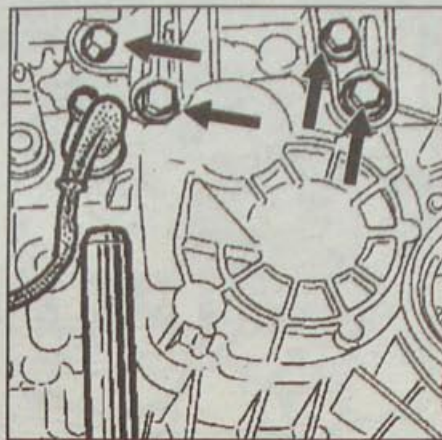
Расположение болтов крепления левой опоры коробки передач
